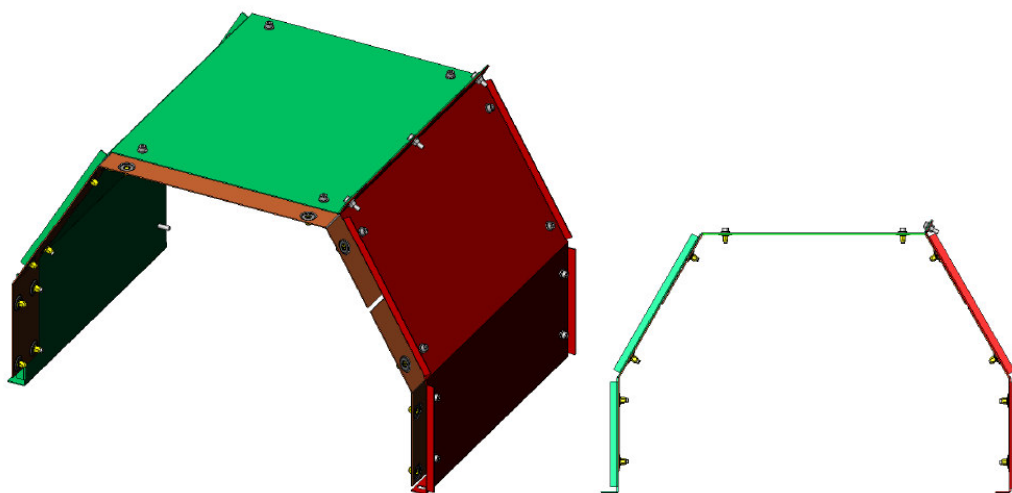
Una soluzione attuale del condotto e vista della sezione frontale
